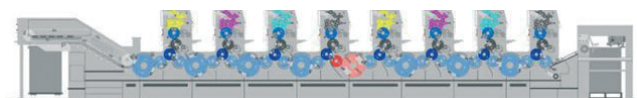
Speedmaster SM 102-Achtfarben-Druckmaschine mit Wendung nach dem vierten Druckwerk; rechts: Anleger; Mitte: 8 Druckwerke; links: Ausleger.
